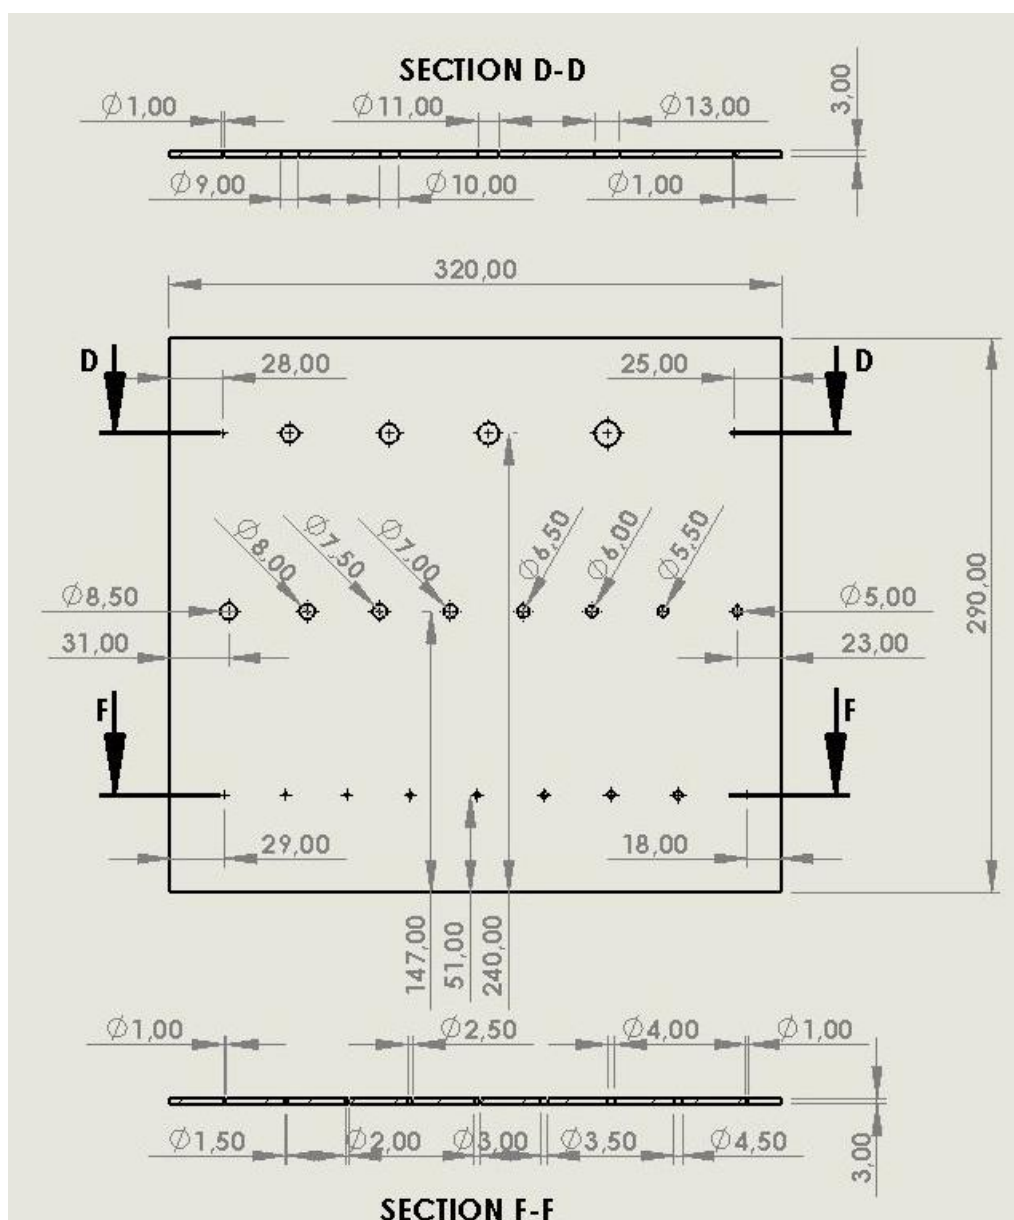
Desenho técnico 2D relativo ao laminado constituído por furos passantes (dimensões em mm).
